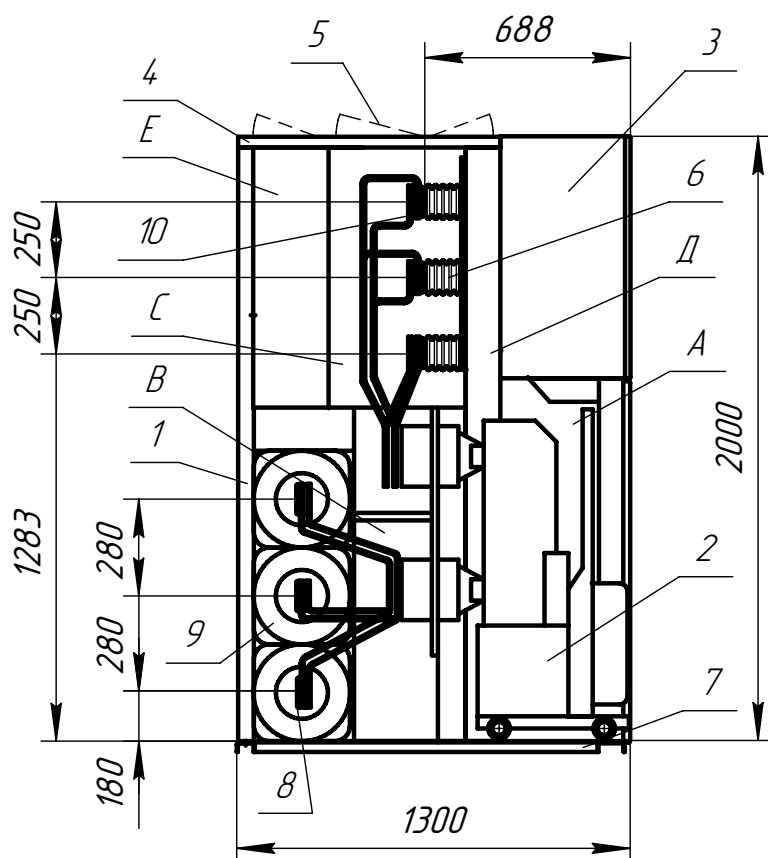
Габаритные, установочные, присоединительные размеры шкафов.
